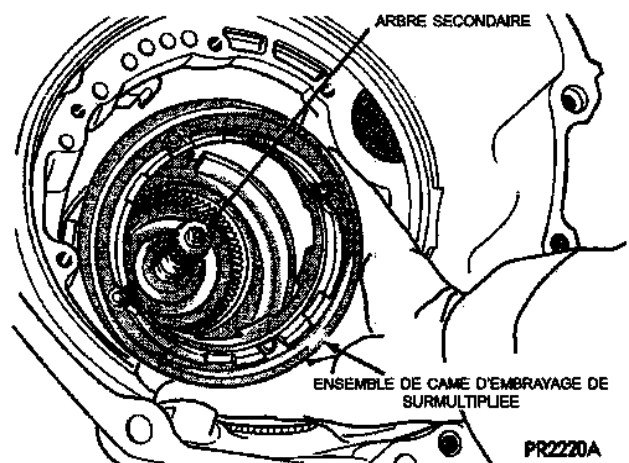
Ensemble de came d'embrayage de surmultipliée
